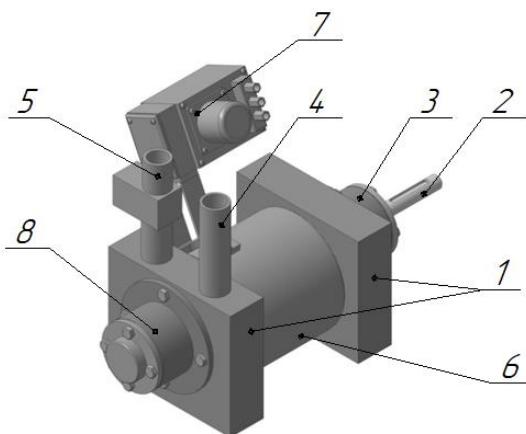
ЖВН с устройством автоматического регулирования нагнетательного окна: 1 – лобавины; 2 – вал; 3, 8 – подшипниковые опоры; 4 – впускной патрубкок; 5 – выпускной патрубкок; 6 – корпус; 7 – нагнетательное устройство.
